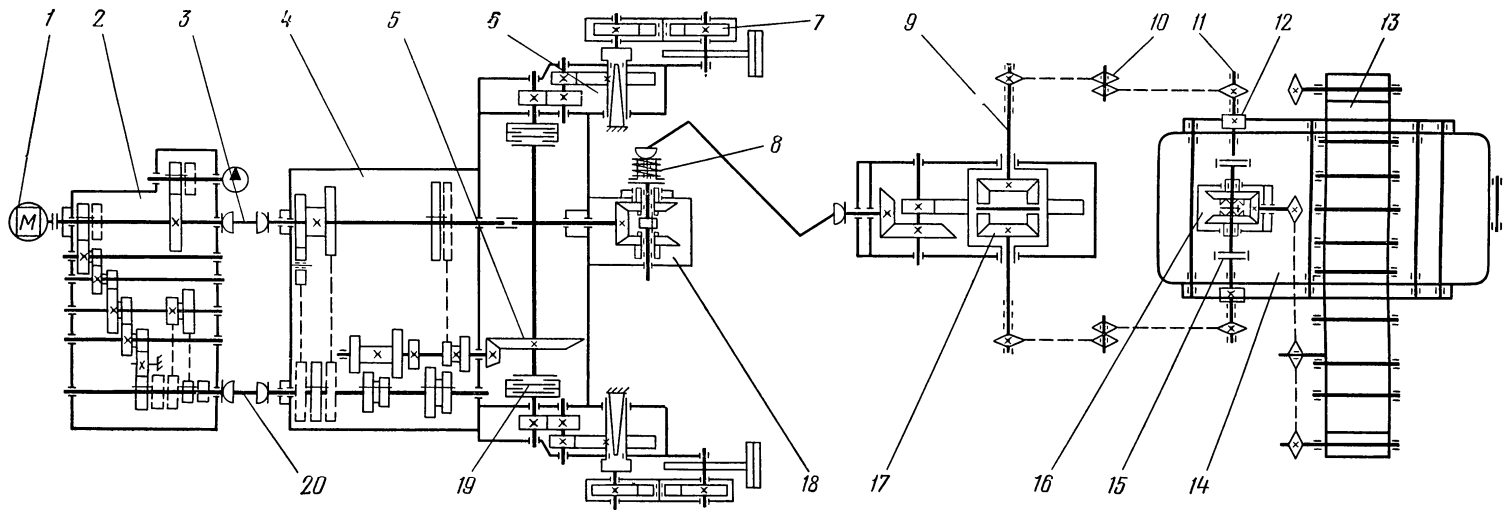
Кинематическая схема экскаваторов ЭР-7АМ и ЭР-7Е:
